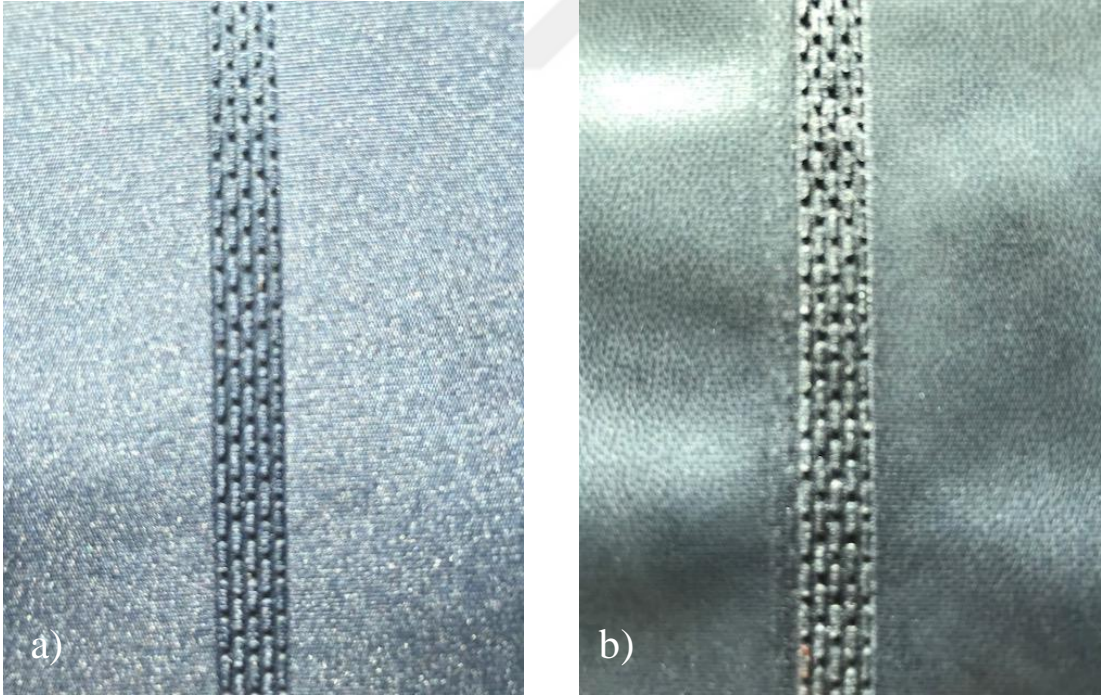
Ultrasonik dikiş makinesinde R2 ile dikilen D1 kumaşının görüntüsü
